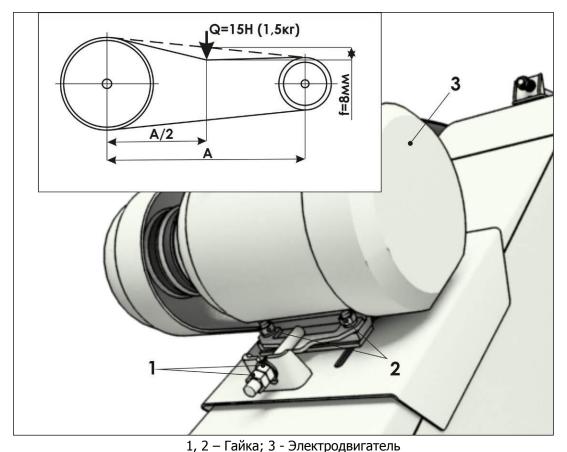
Регулировка натяжения клиноременной передачи привода загрузочного транспортера
